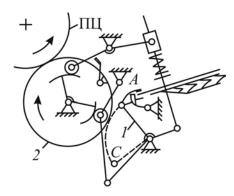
Схема механизма нижнего качающегося форгрейфера: 1 – рычаги форгрейфера; 2 – передаточный цилиндр; ПЦ – печатный цилиндр
